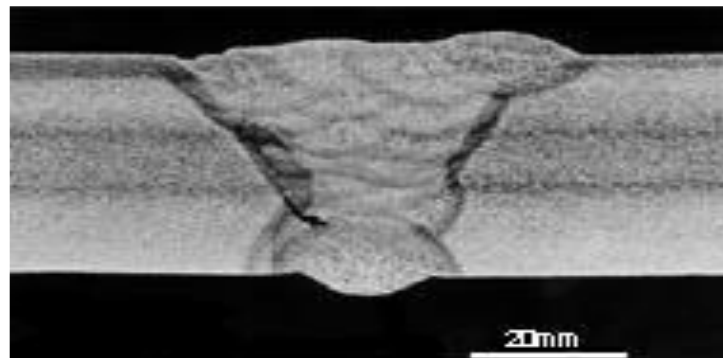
Manque de fusion dans le flanc de la soudure. [11]
